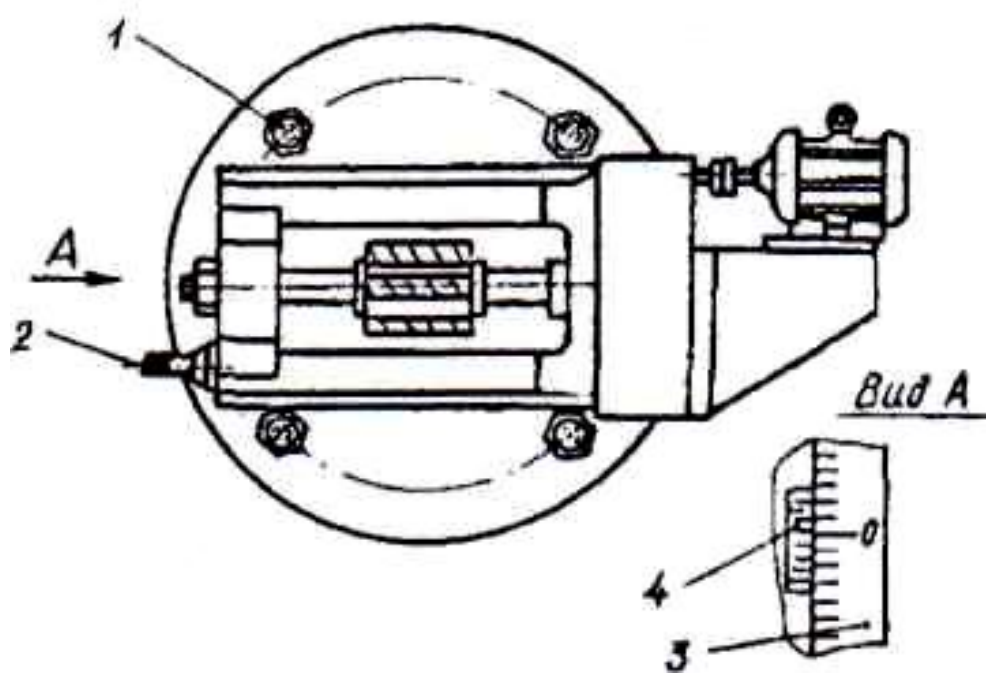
Схема встановлення фрезерного супорту на розрахований кут
